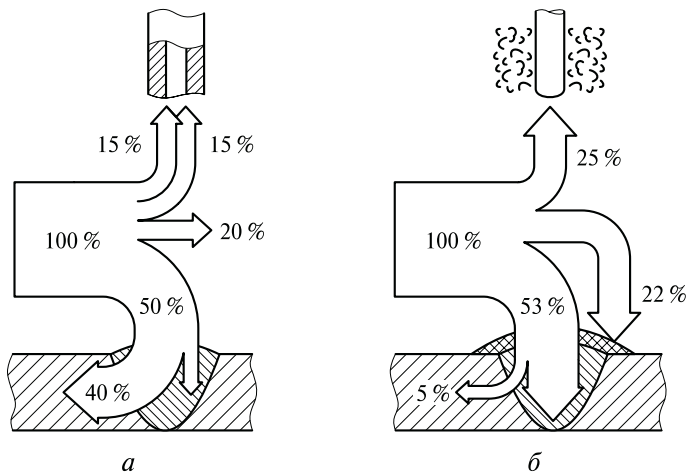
Тепловой баланс дуги при сварке:
